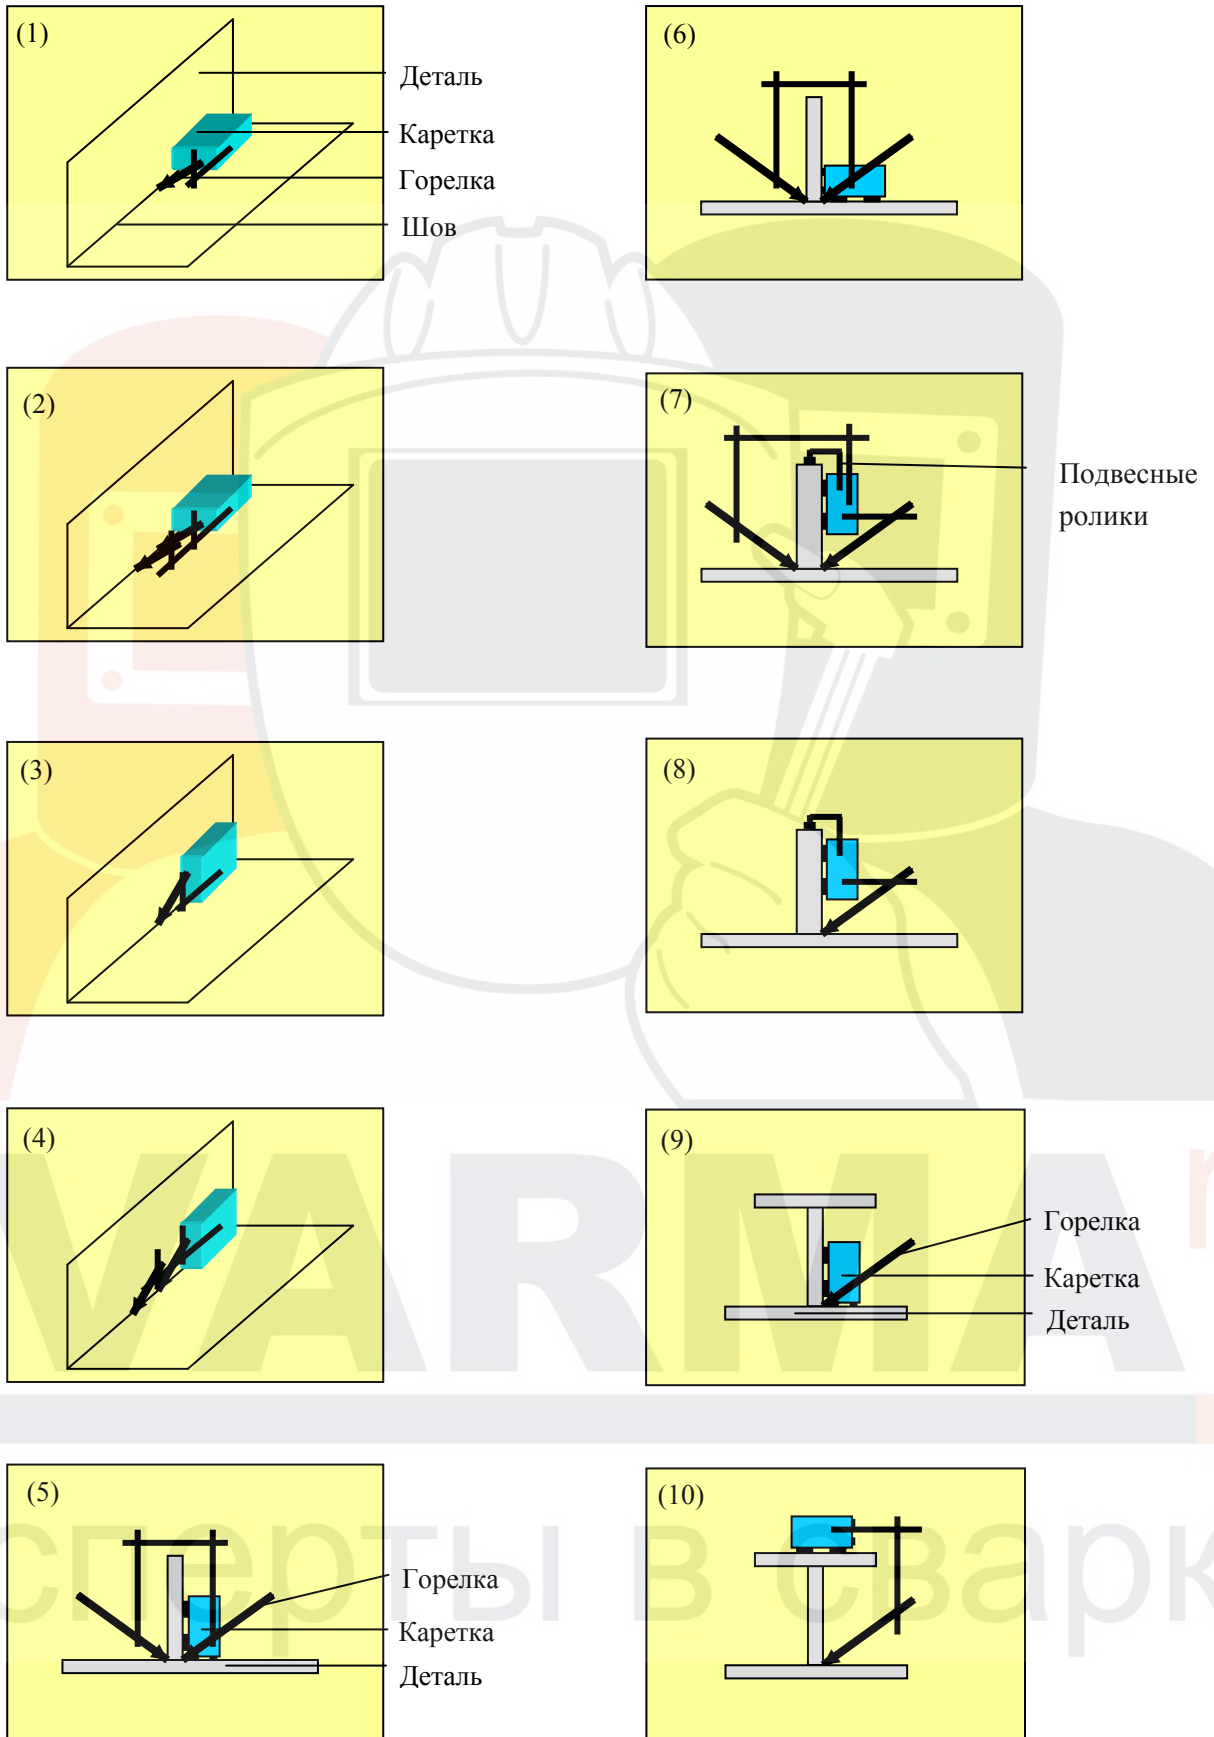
Примеры применения сварочной каретки НТТ-18-1SD-2
